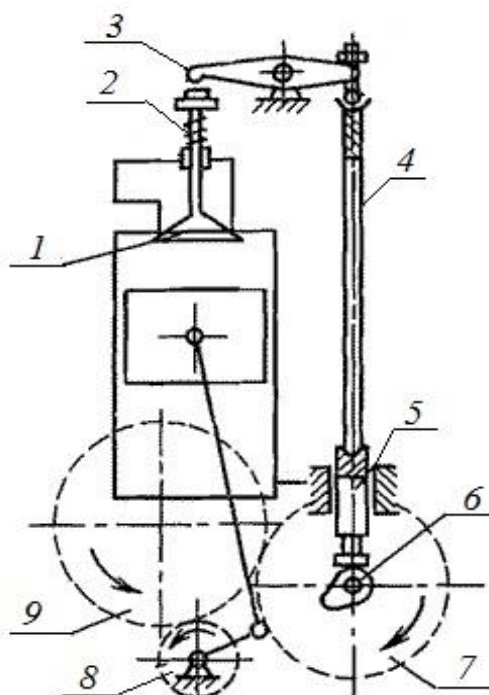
Механизм газораспределения ДВС с приводом зубчатыми колесами
